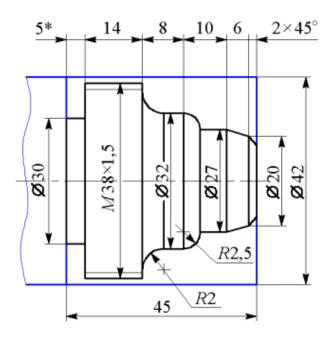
Эскиз обрабатываемой детали для подгруппы 2
